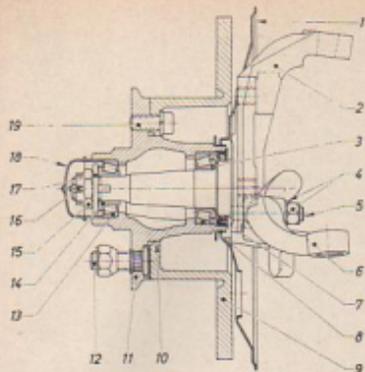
Vorderradnabe mit Bremscheibe auf Achschenkeln aufgeschraubt
